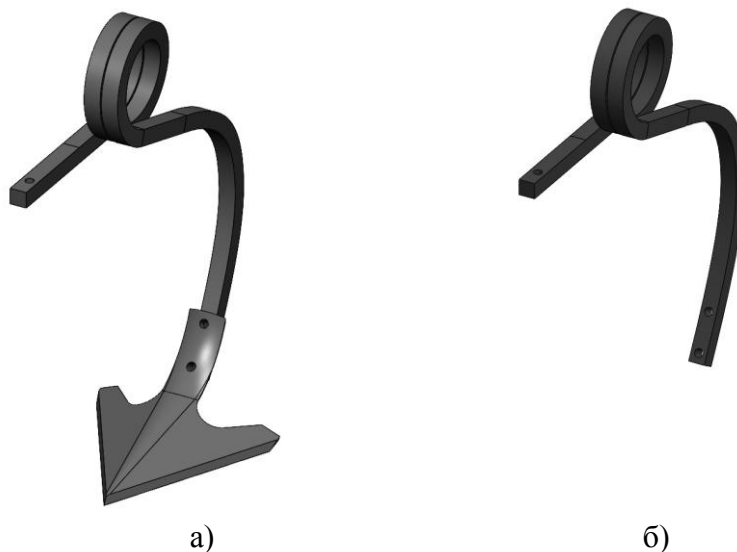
CAD-модель двовиткової спіральної стійки з культиваторною лапою
